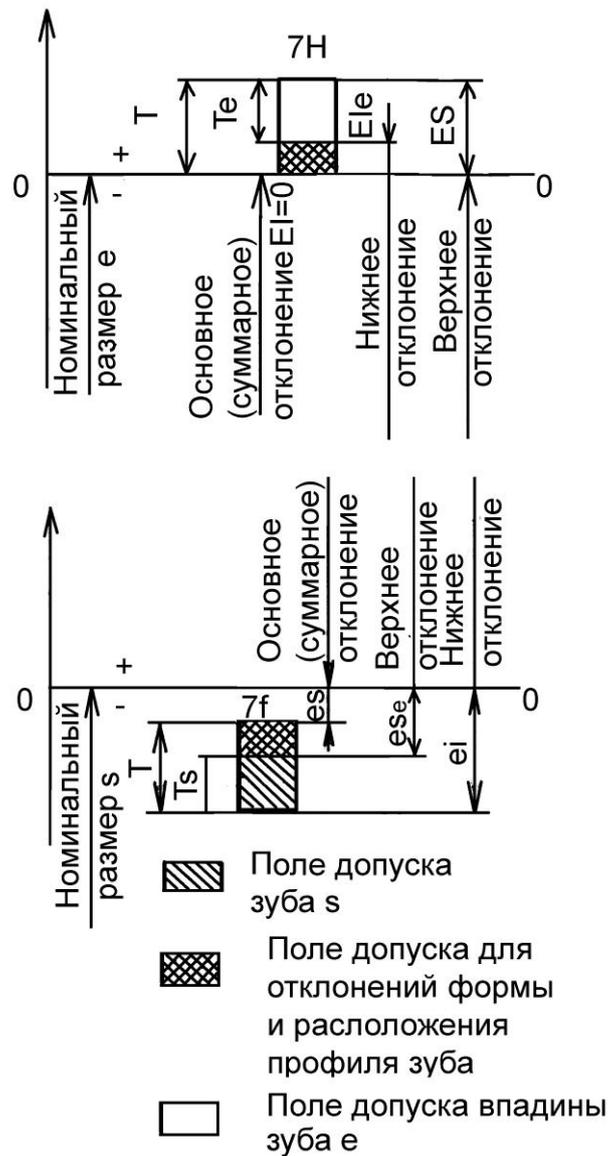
Расположение полей допусков толщины зуба s и ширины впадины e эвольвентного шлицевого соединения.
